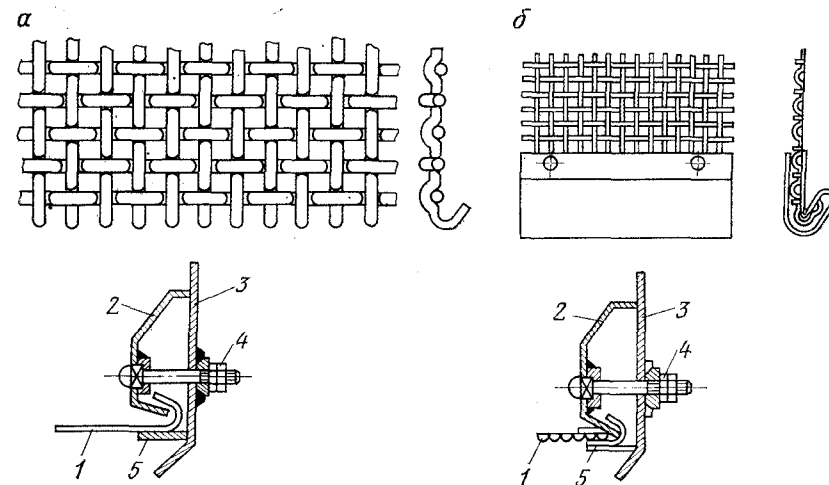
Детали для поперечного натяжения сит на коробе грохота: а — крепление сетки из проволоки диаметром 4,5—10 мм; б — то же, из проволоки диаметром 1,8—3 мм
